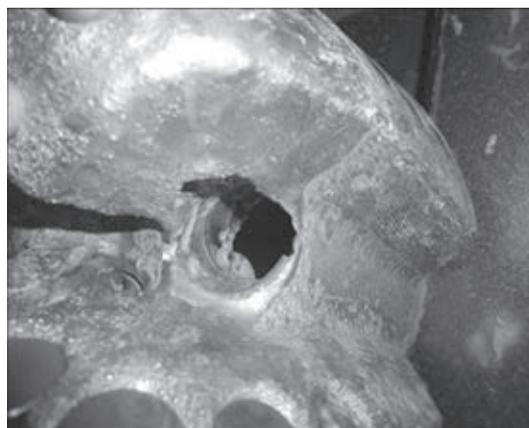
Внешний вид износа рабочего органа промывочного канала стального корпуса с упрочняющим защитным покрытием
